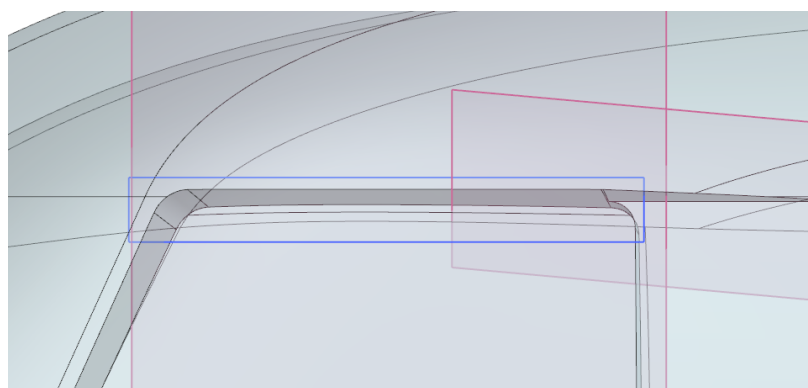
Эскиз установочной поверхности блистера сдвижного
